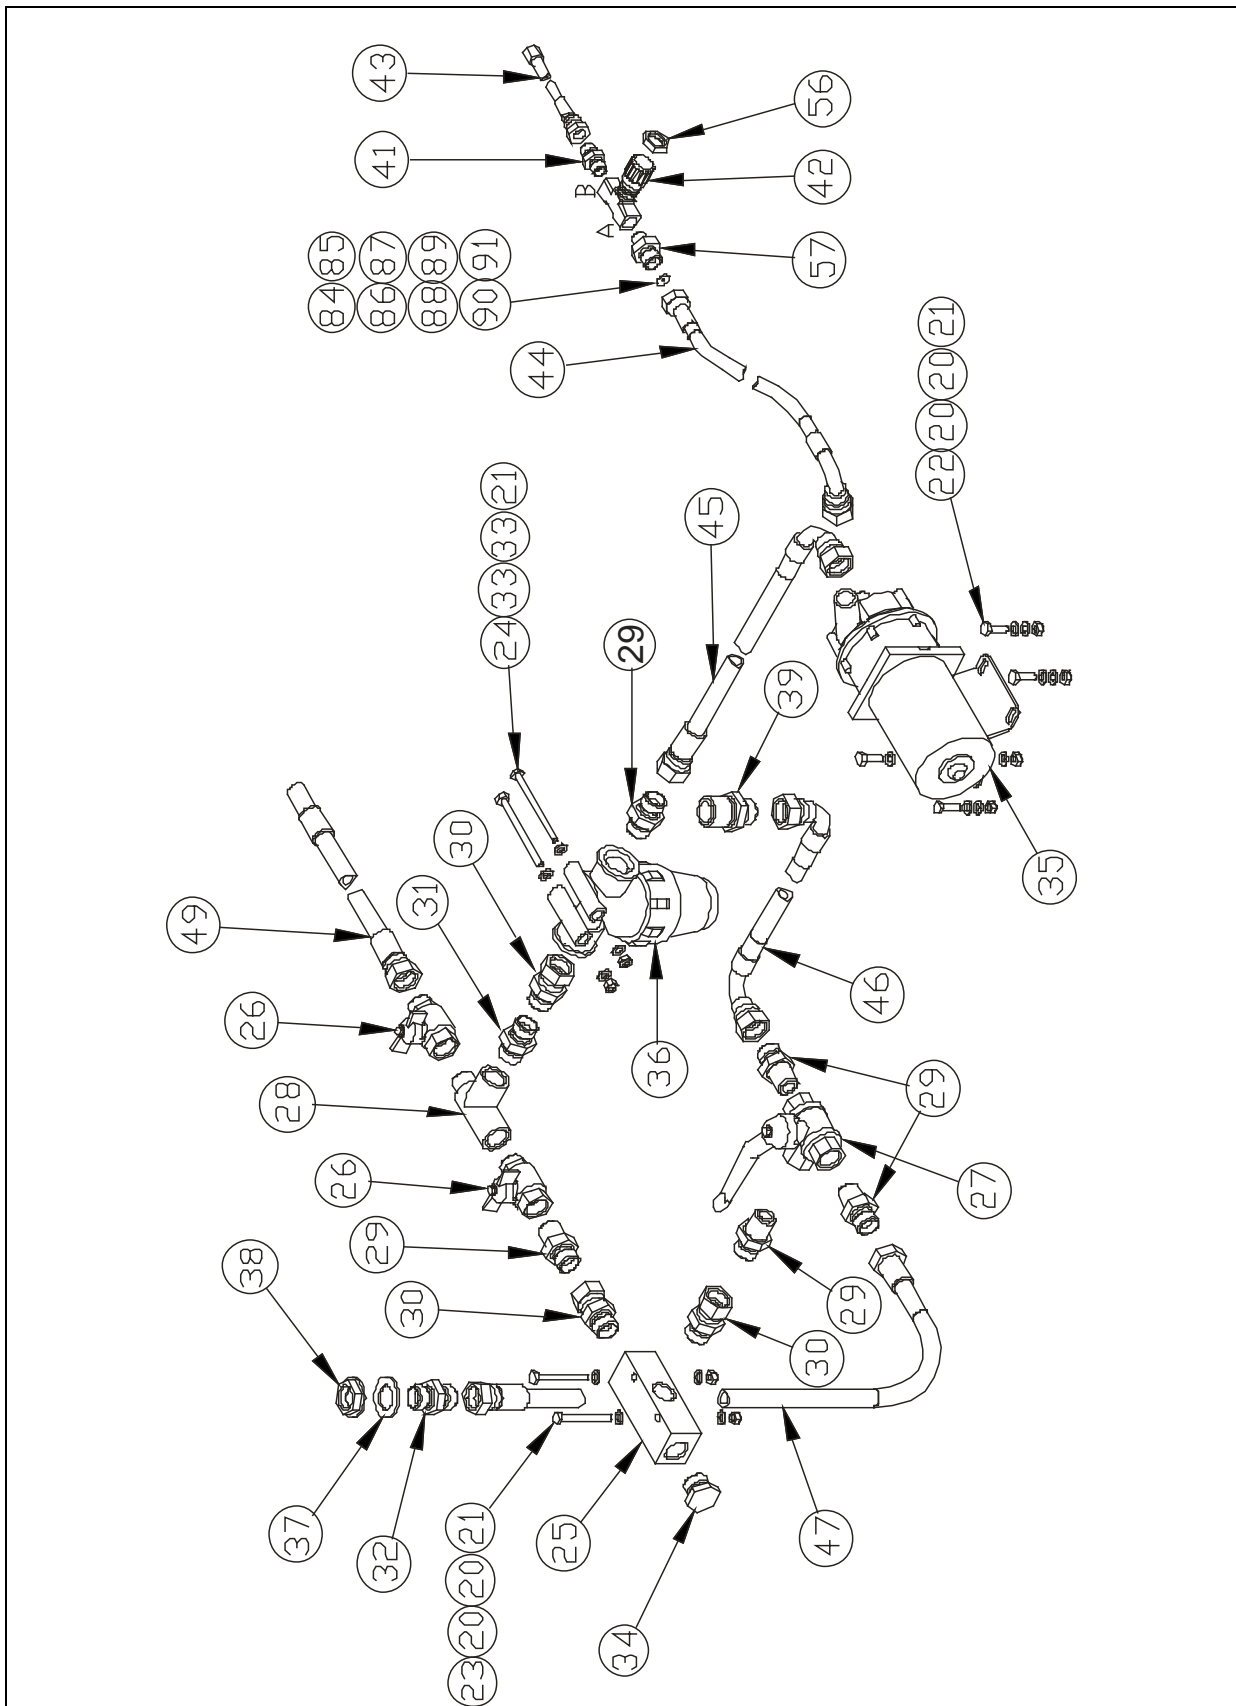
Pièces de tuyauterie AU 8115MS (Continué)
